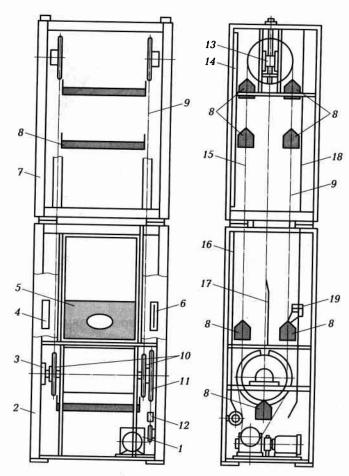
Механизированный стеллаж элеваторного типа:
